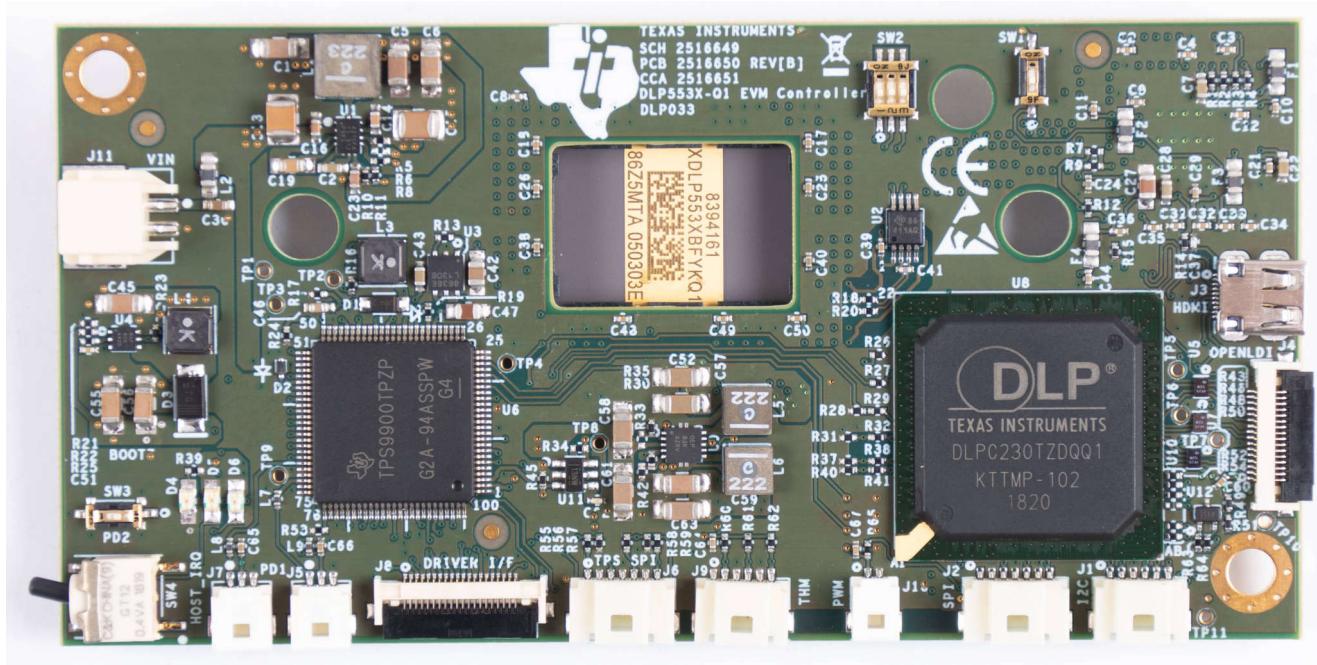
DLP5532PROJHBQ1EVM 控制器 PCB
